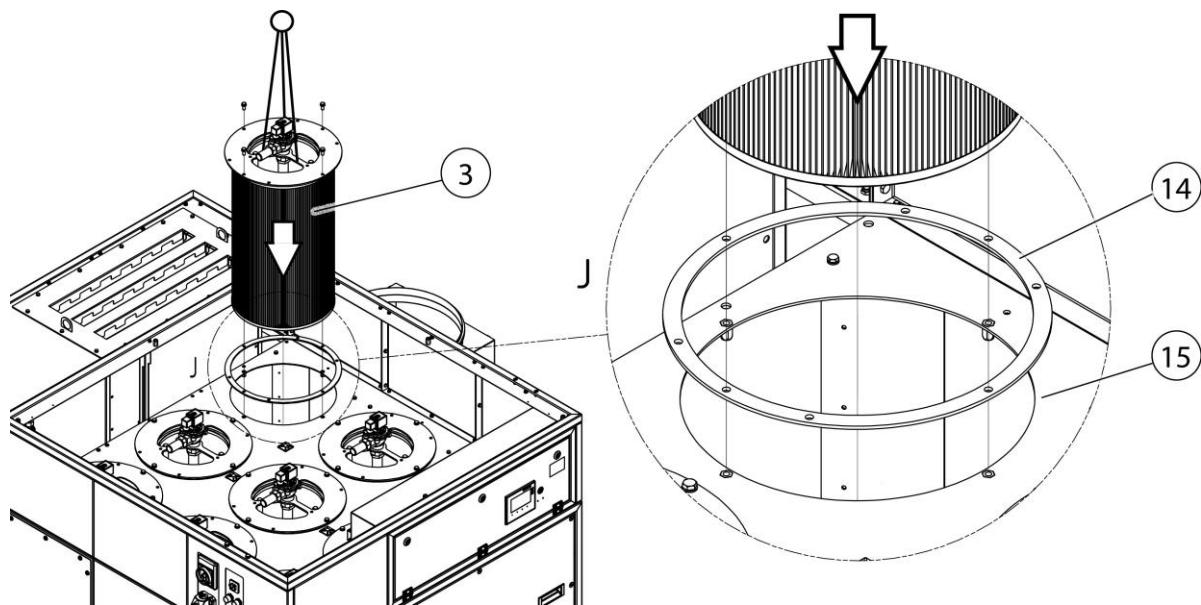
Remplacement du filtre – Joint d'étanchéité du porte-filtre
